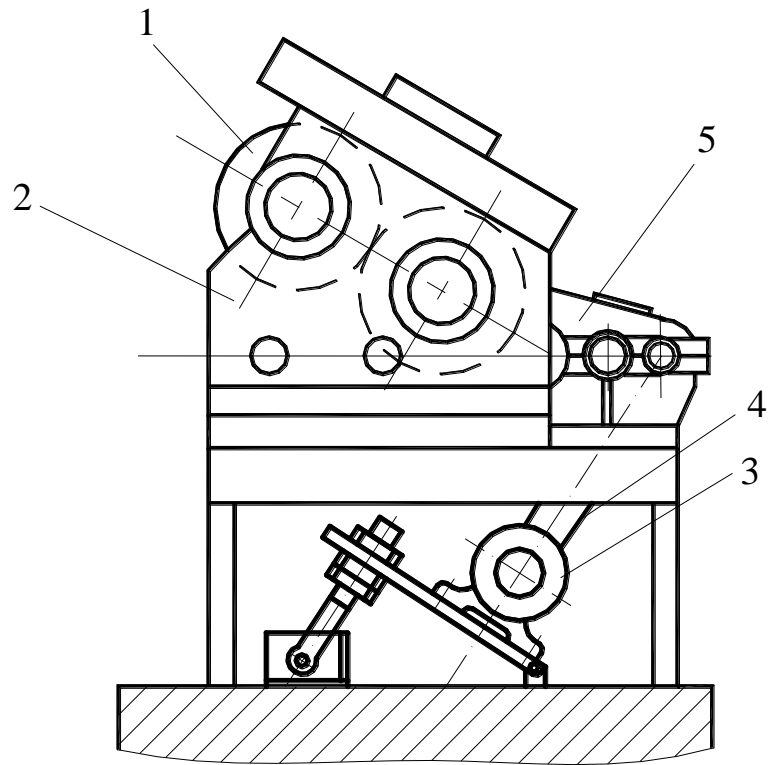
Схема прокатного стана для прокатки порошков
